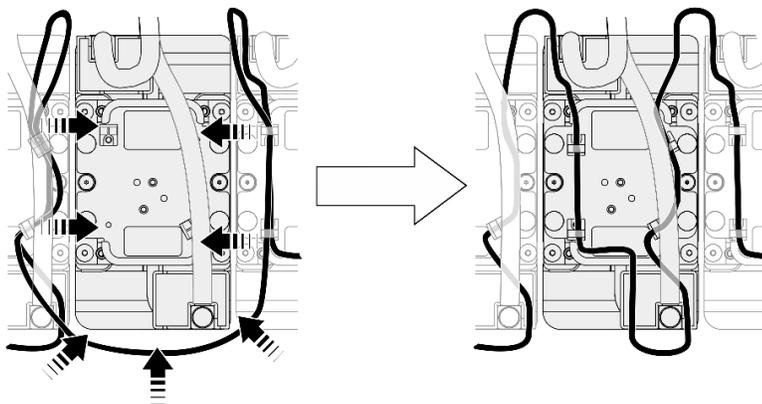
Instalando o cabo do módulo do sensor de vazamento
